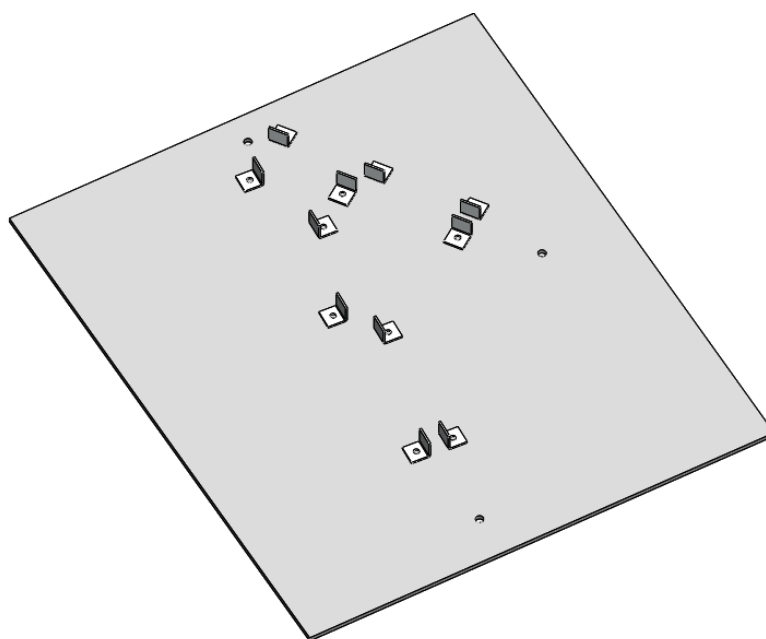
Общий вид кондуктора для сборки поперечных рычагов
